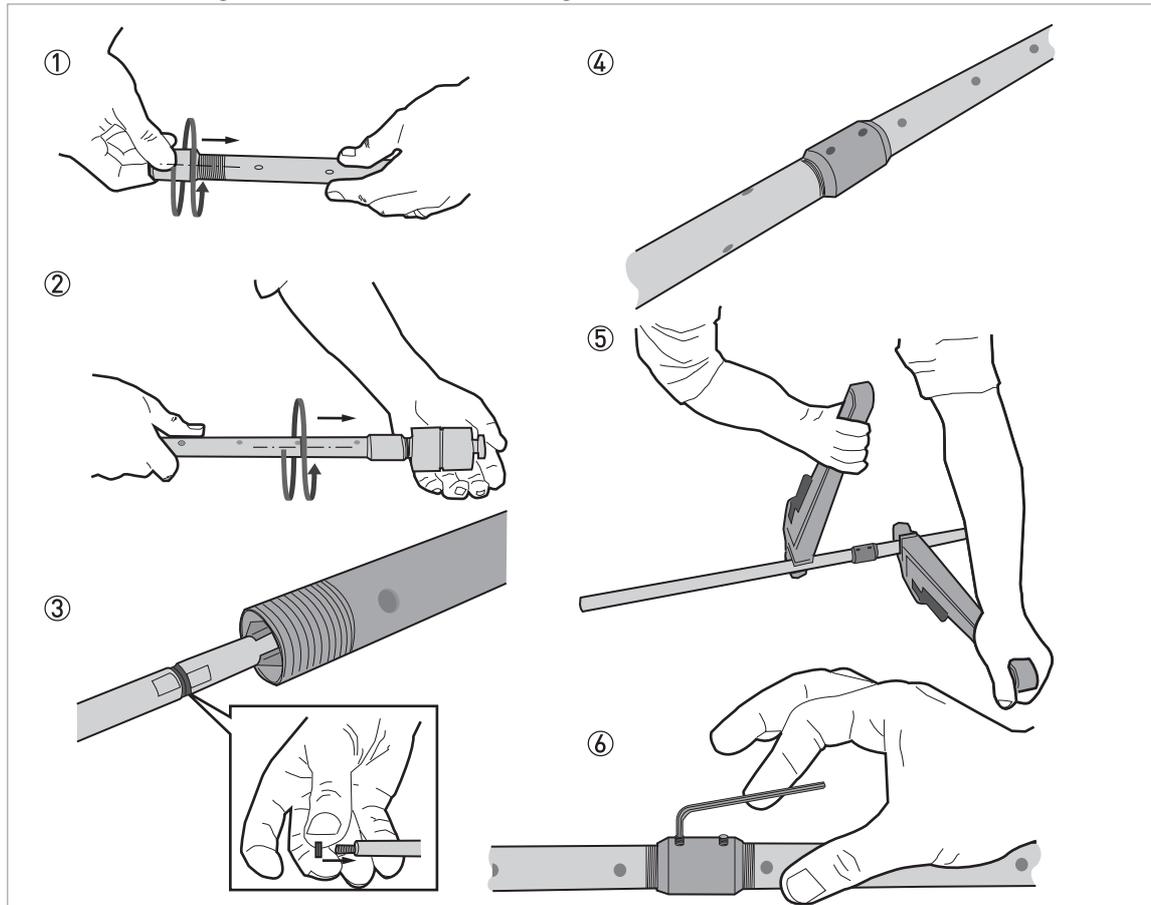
Montage de la sonde coaxiale segmentée : partie 2
